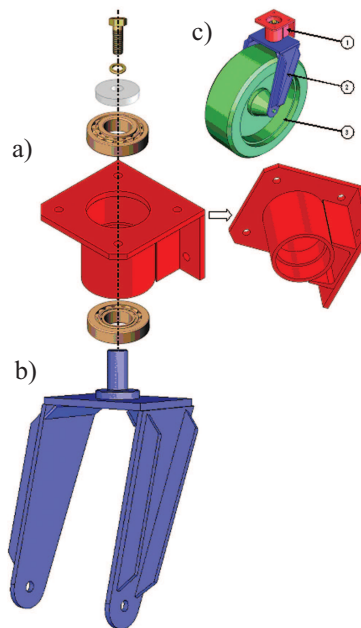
Widok na elementy przyłączeniowe modelu 3D konstrukcji nośnej sadzarki zagonowej 3-rzędowej
